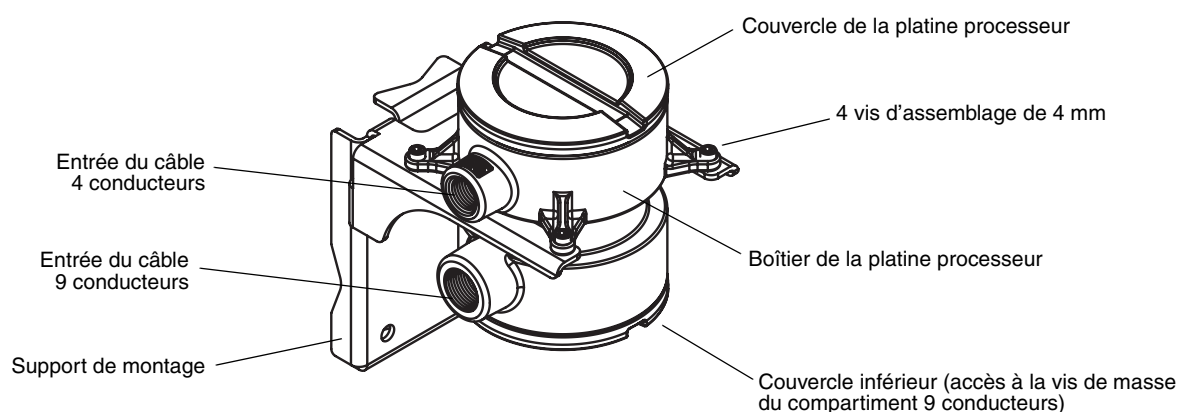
Platine processeur déportée – Montage sur paroi ou sur tube support
